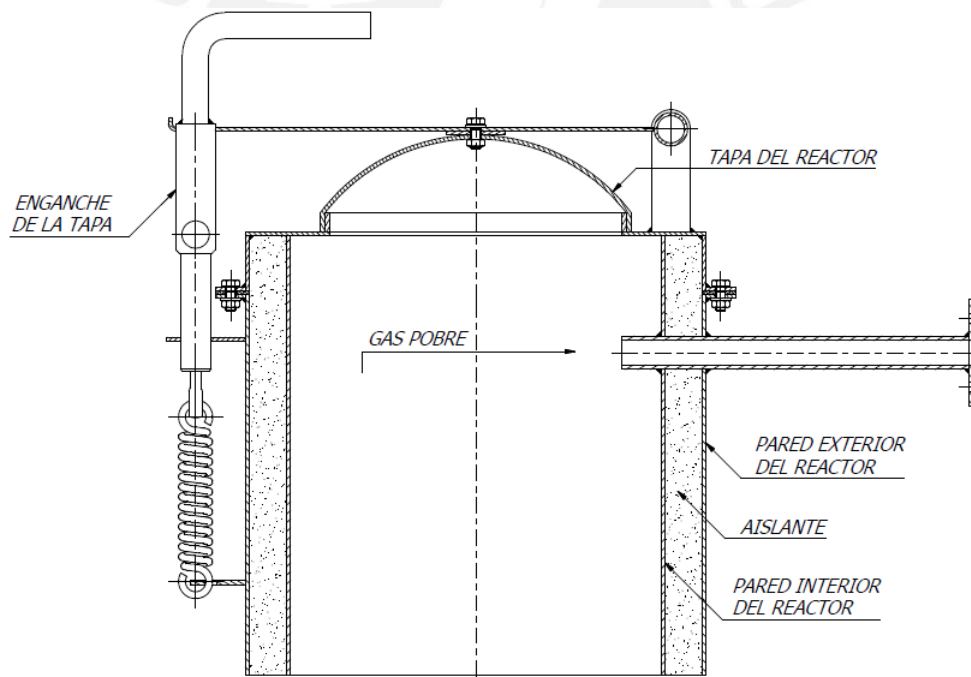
Corte del ensamblaje del reactor y tapa.
